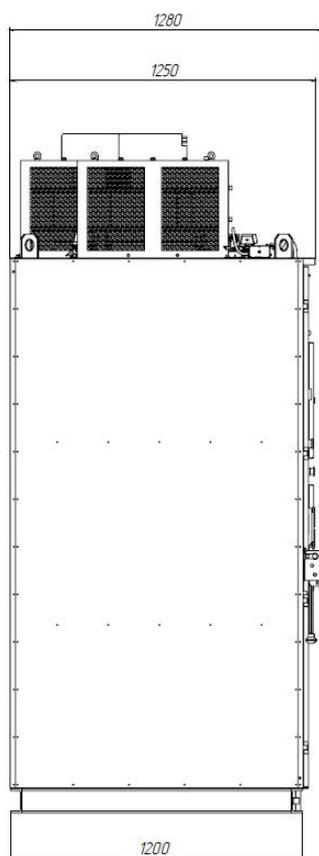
АТ27-М80...1М6-6/6-XXXXXX-С-43. Вид сбоку
